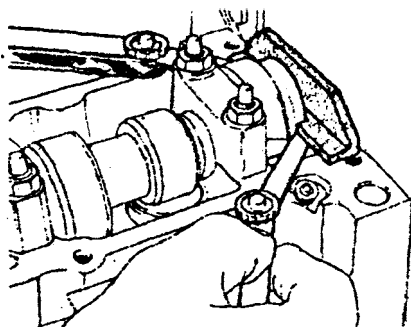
Установка приспособления для фиксации распределительного вала
